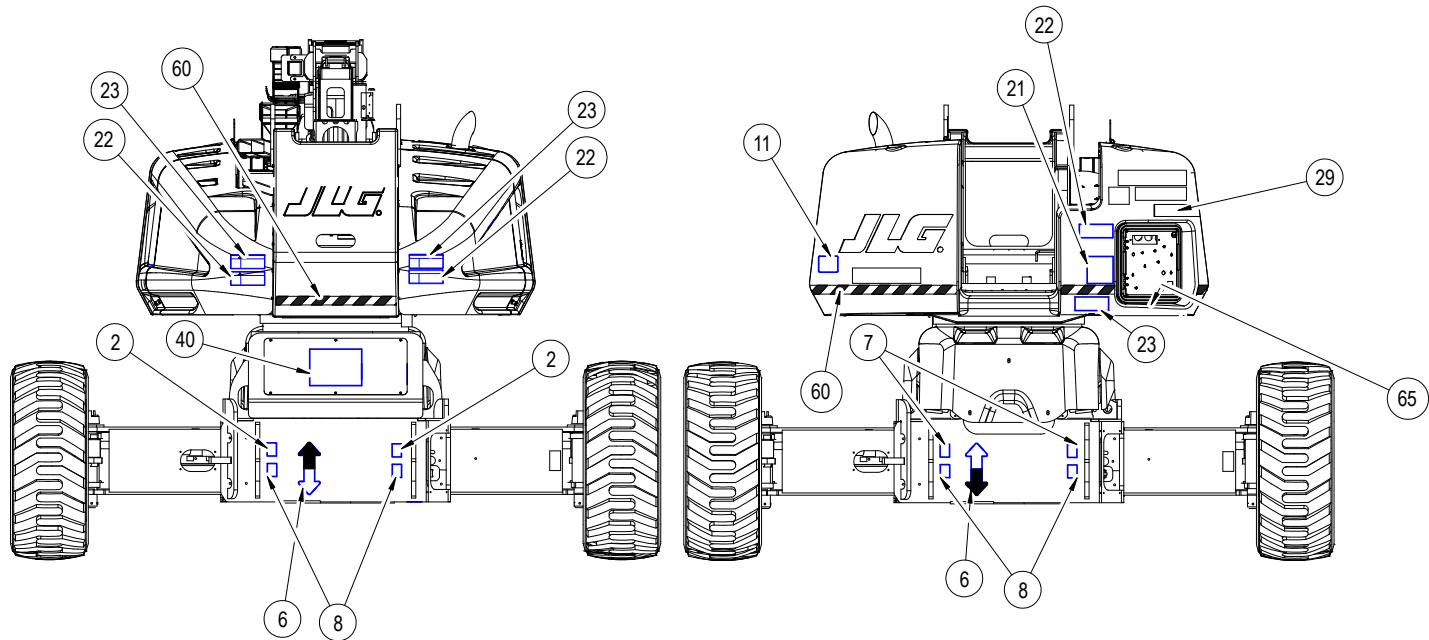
Dekalplacering - Serienummer 0300141446 till nu - Endast CE - Blad 5 av 5
